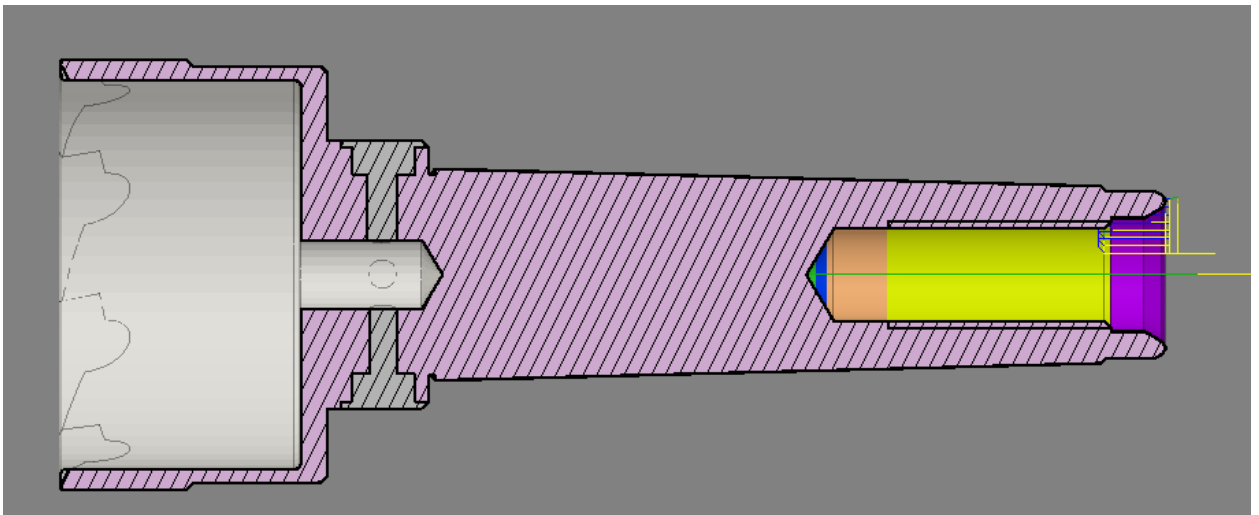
Обробка внутрішнього отвору конуса
